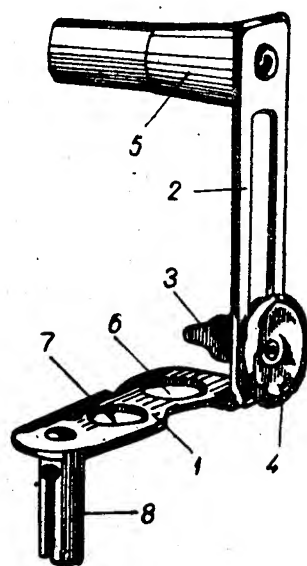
Универсална диафрагма: 1 — основание; 2 — стойка; 3 — переставляемая ключалка; 4 — подвижный окуляр; 5 — трубка за закрепление к пушке; 6, 7 — круглые отверстия за закрепление к картечнице; 8 — шип за закрепление на диафрагма к старите образцы тяжелых картечниц
